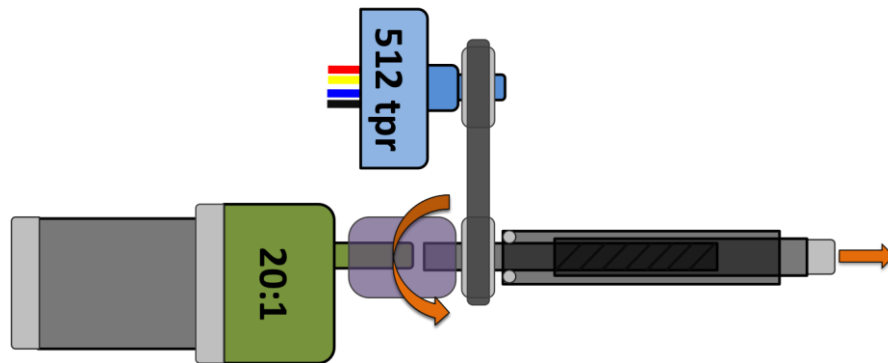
Esquema da alternativa a) para encoder elevação.
